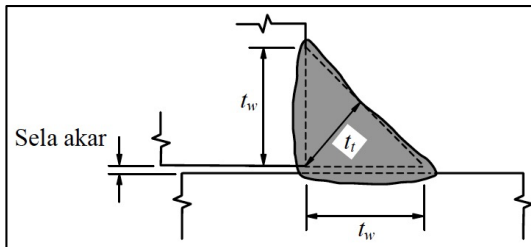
Las Sudut (*Fillet Welds*)
